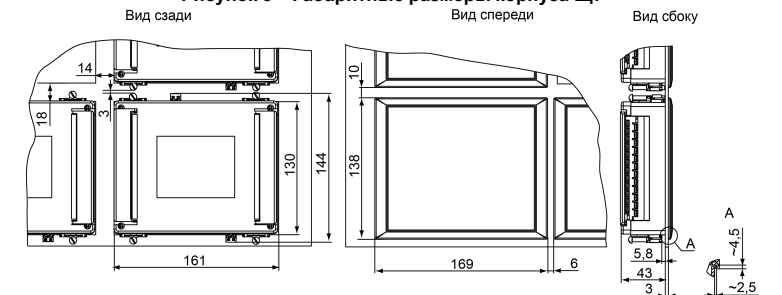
Прибор в корпусе Щ7, установленный в щит толщиной 3 мм
